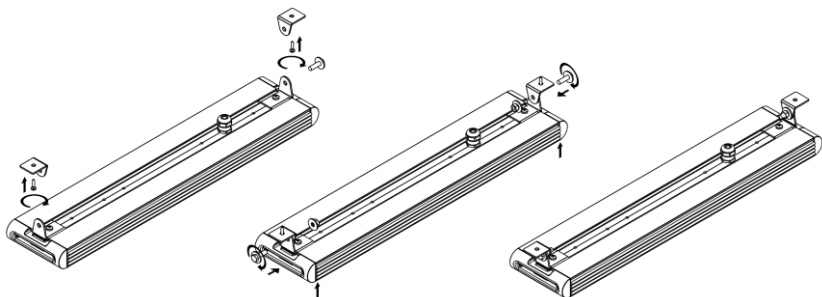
Установка светильника при помощи крепления Уголок для накладного монтажа.
